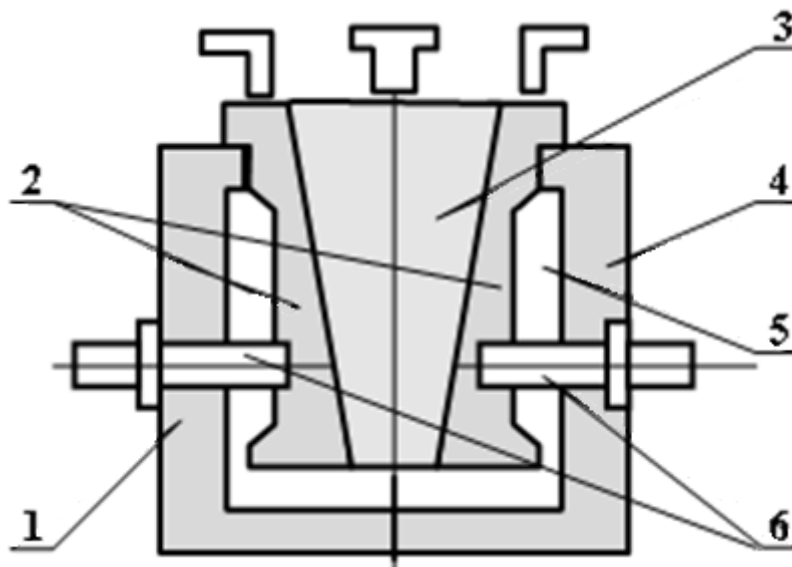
Схема кокиля с вертикальным разъемом для отливки поршня автомобильного двигателя:
